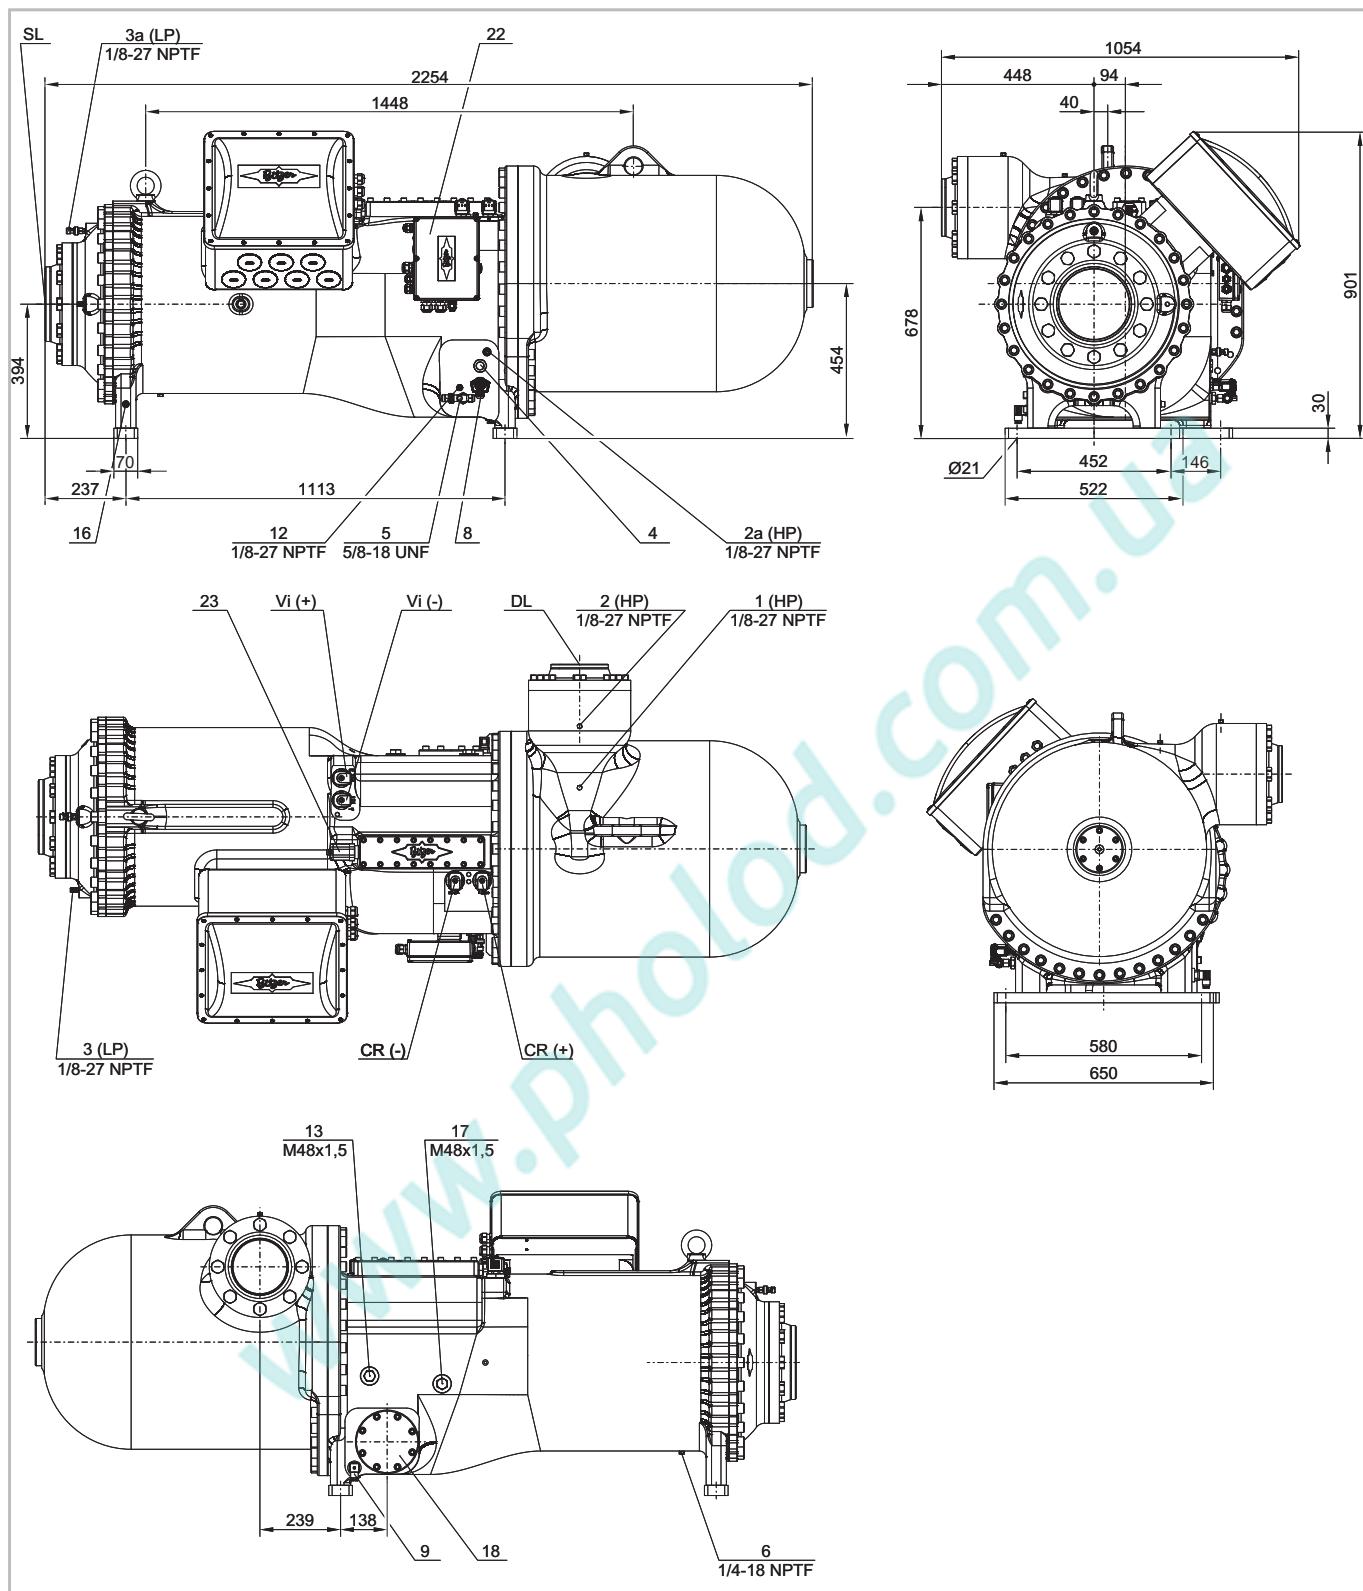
Чертежи с указанием размеров для компрессоров CSW10593-400Y
